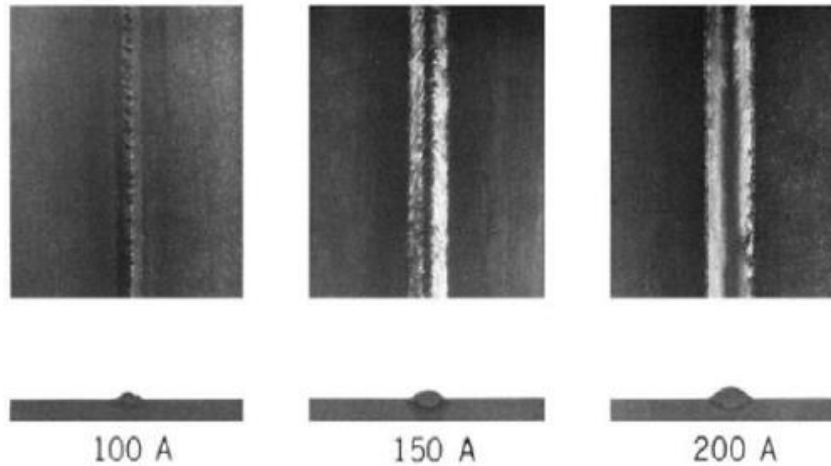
Efeito da corrente de soldadura na penetração da solda – aço carbono, curto-circuito, Ar-25%CO₂ [29].
